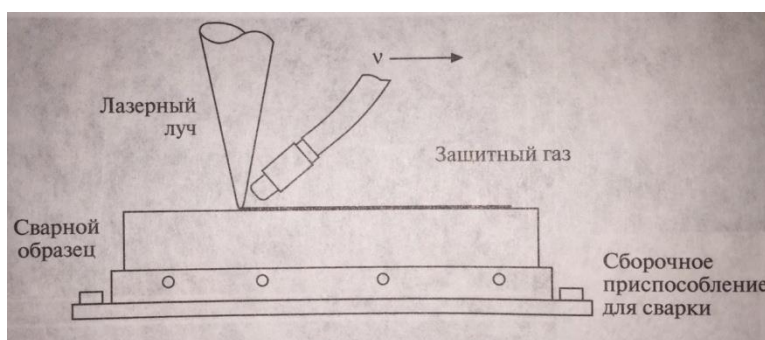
Схема лазерной сварки, защитный газ предотвращает окисление поверхности в процессе сварки
